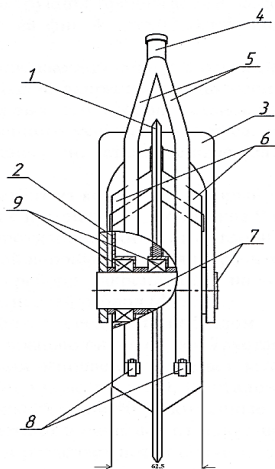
Однодисковый сошник с двухсторонними ребрами-бороздкообразователями для узкорядного посева: 1 – плоский диск; 2 – реборда; 3 – корпус; 4 – делительная воронка; 5 – семянаправители; 6 – чистики; 7 – ось; 8 – клапаны; 9 – подшипники
